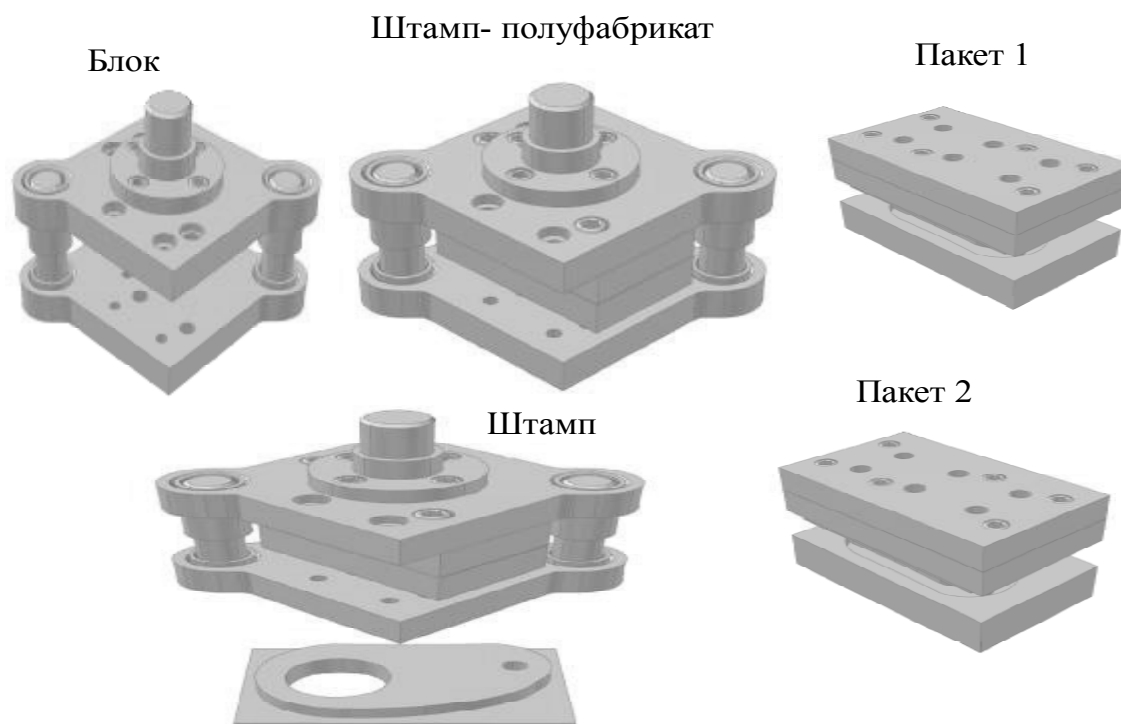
Модель композиции штампа для детали заказчика на базе штамп - полуфабриката
